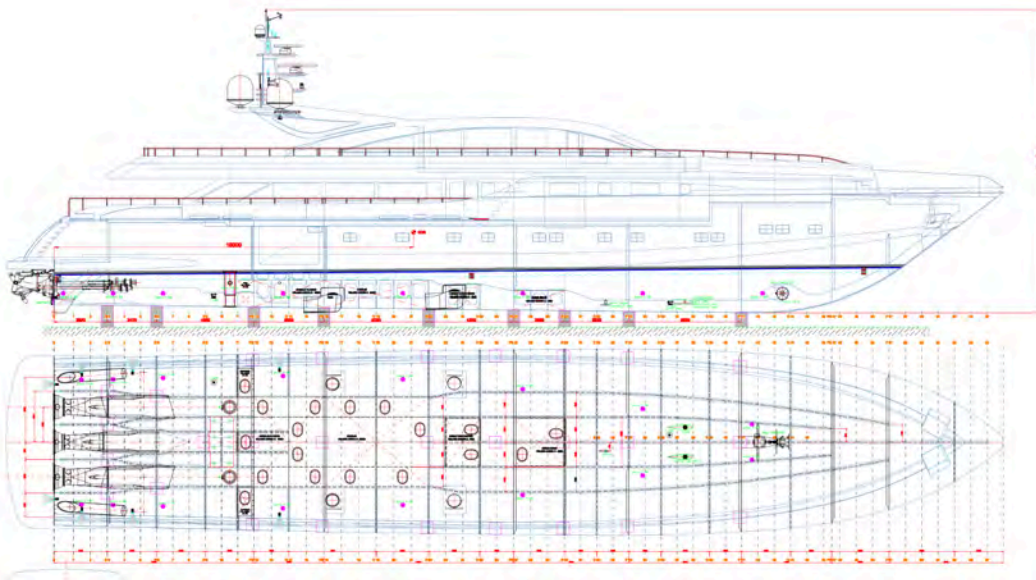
Plano ubicación de estabilizadores (Fuente: Trabajo de campo)
